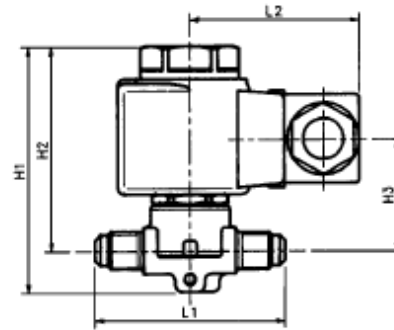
Desenho da válvula solenoide Castel 1020.
